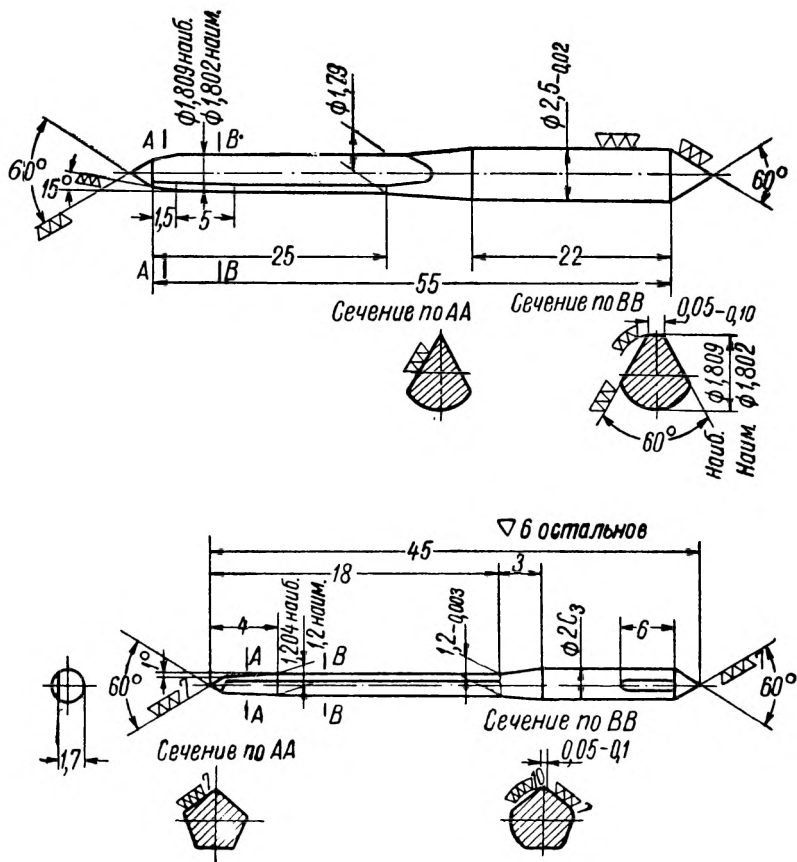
Развертки, применяемые для чистовой обработки малых отверстий.
